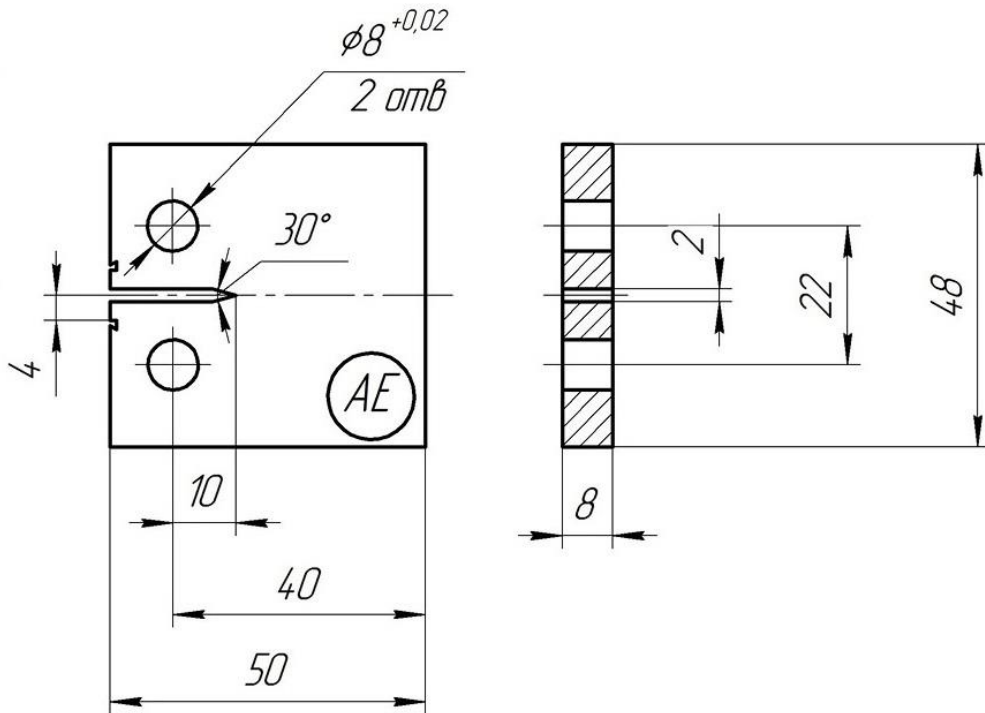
Чертеж образца ТРИП/ТВИП стали для испытания на рост усталостной трещины; место расположения датчика АЭ обозначено «АЭ»
